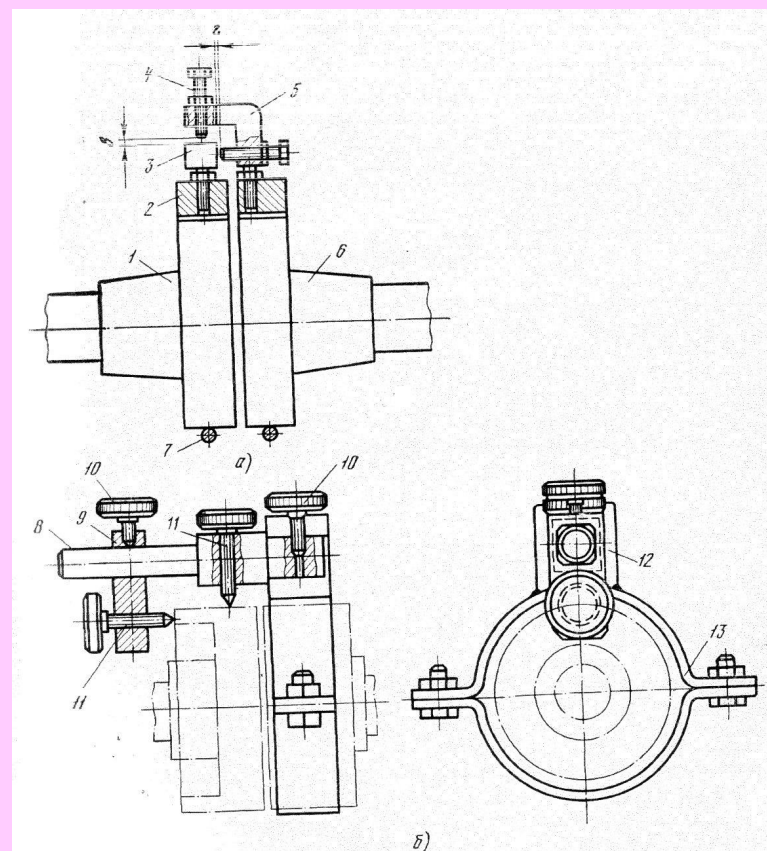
Проверка качества установки электродвигателя и машины при непосредственном соединении муфтой с помощью приспособлений, состоящих из хомутов. б — из полуколец; 1 — полумуфта машины, 2 — центровочное приспособление, 3 — квадратная головка, 4 — болт с микрометрической резьбой, 5 — кронштейн, 6 — полумуфта электродвигателя, 7 — хомут, 8 — направляющая штанга, 9 — ползунок, 10 — стопорные винты, 11 — регулировочные винты, 12 — стойка, 13 — сменная полукольцо
